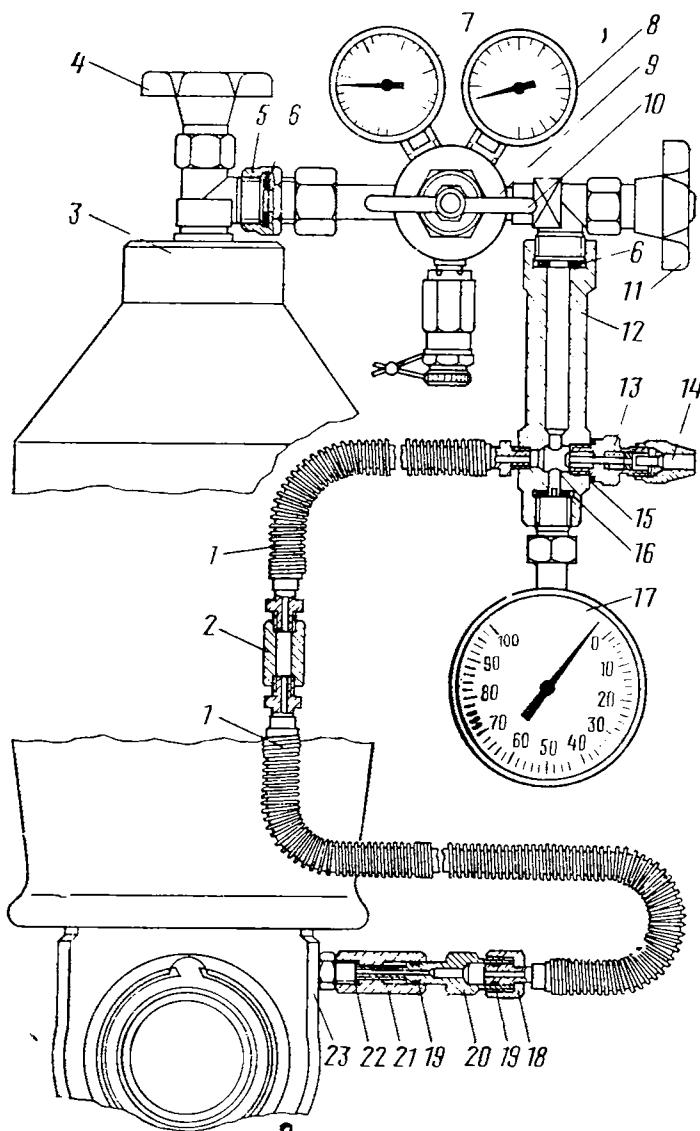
Приспособление для зарядки цилиндров подвески газом:
